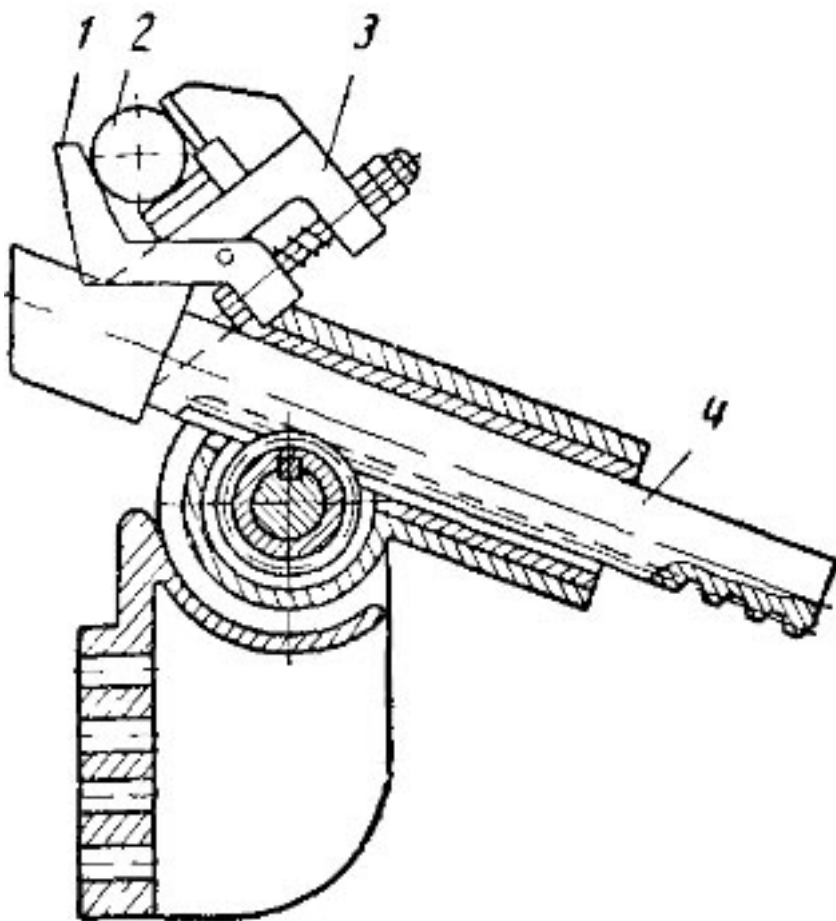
Схема питателя автоматической линии для обработки ступенчатых валов
